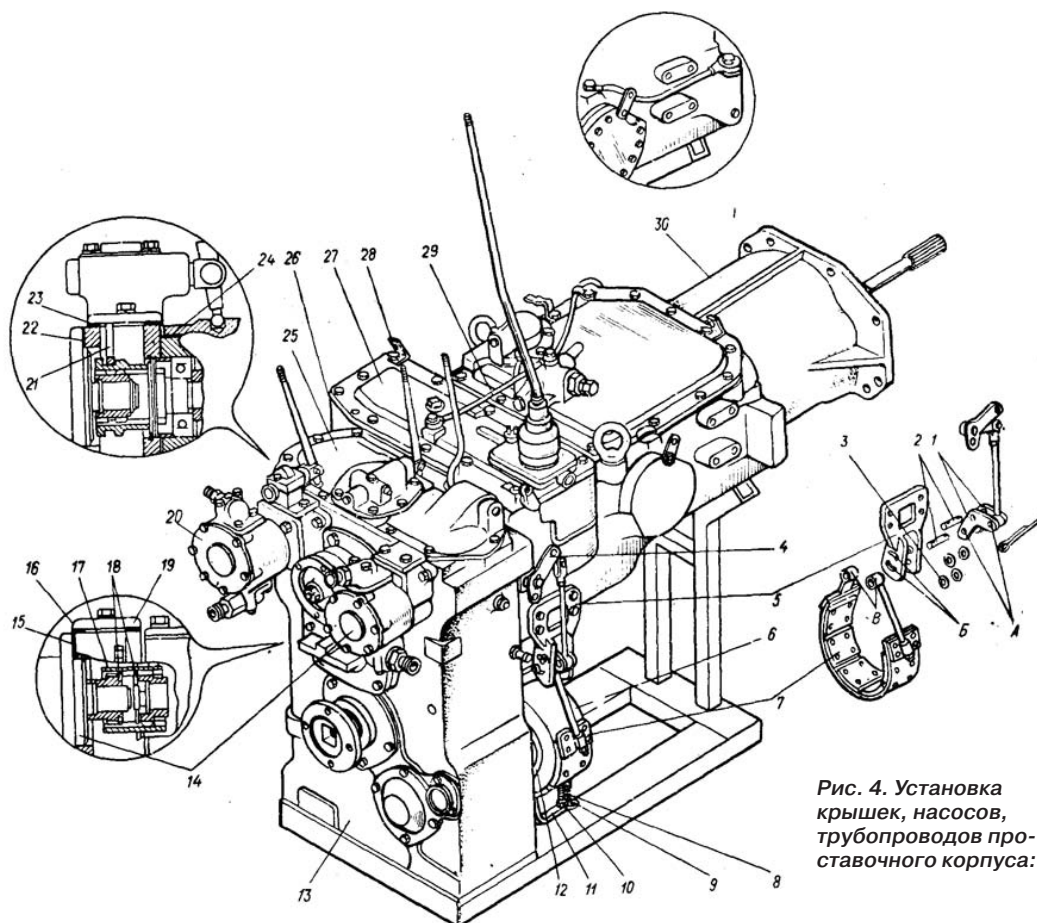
Установка крышек, насосов, трубопроводов, проставочного корпуса:
